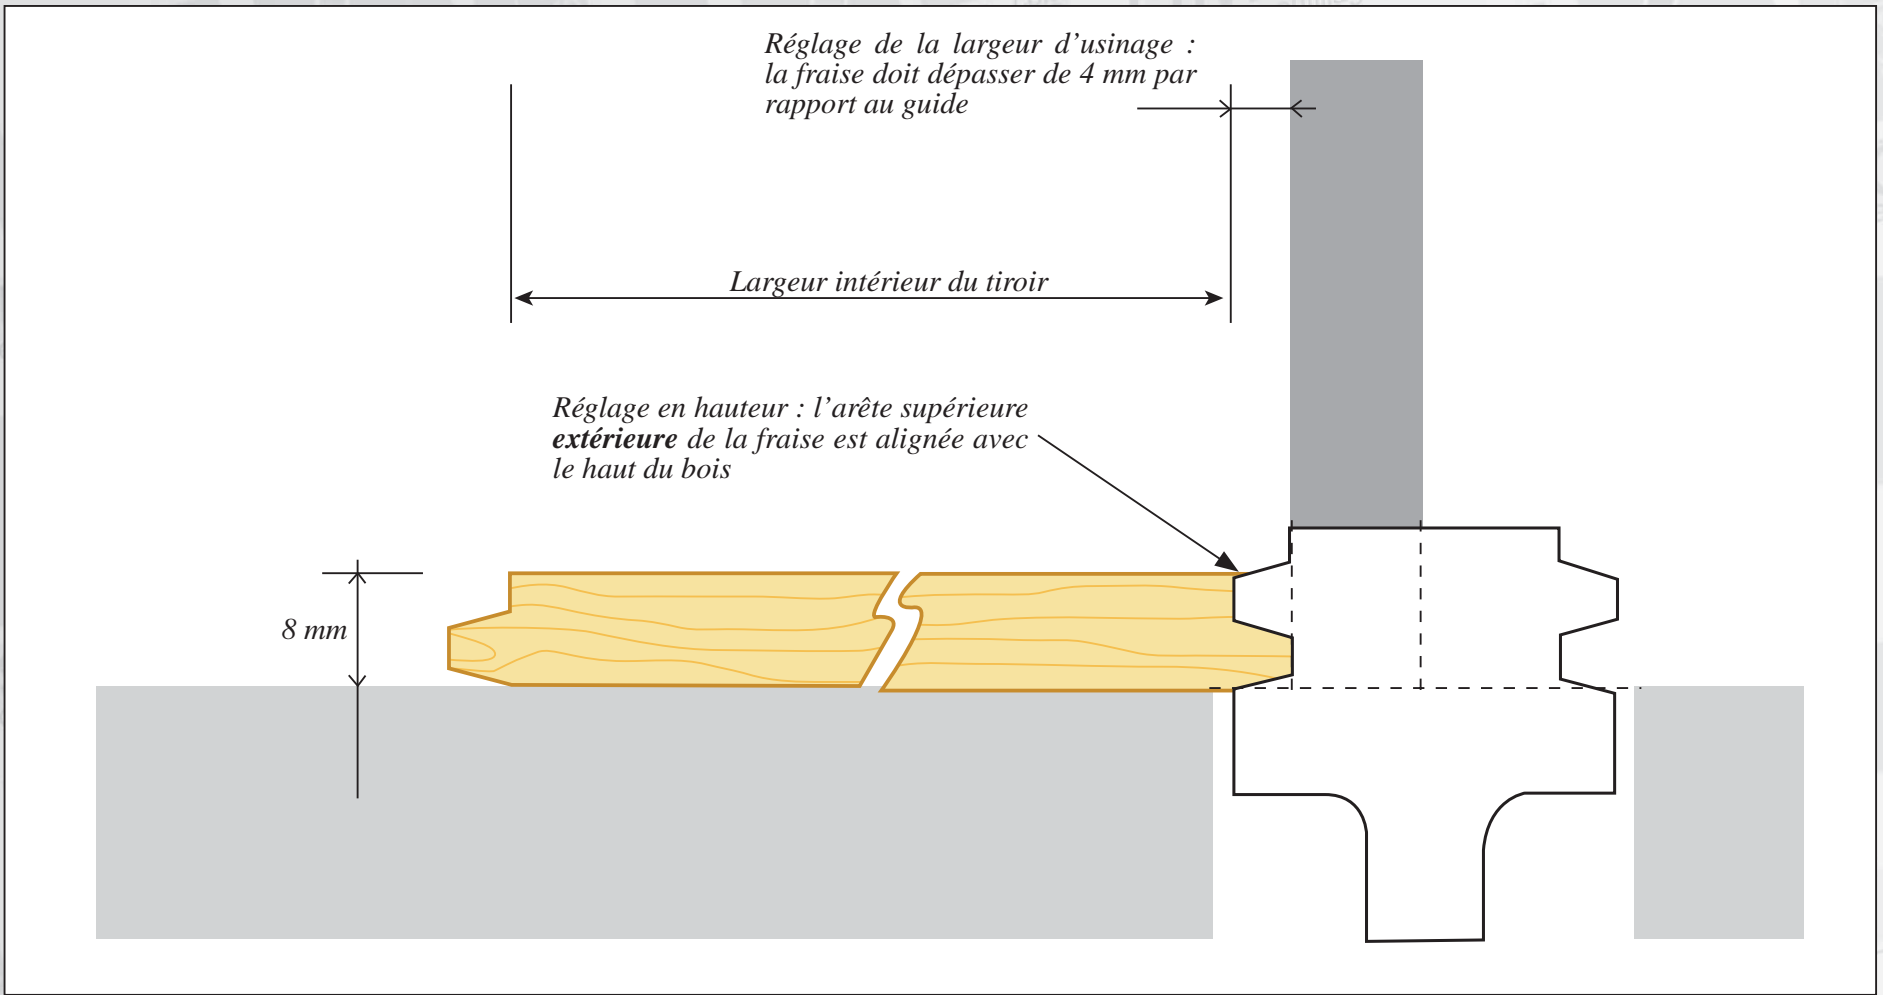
réglage de la fraise pour l'usinage de la façade et de l'arrière (en 8 mm)
